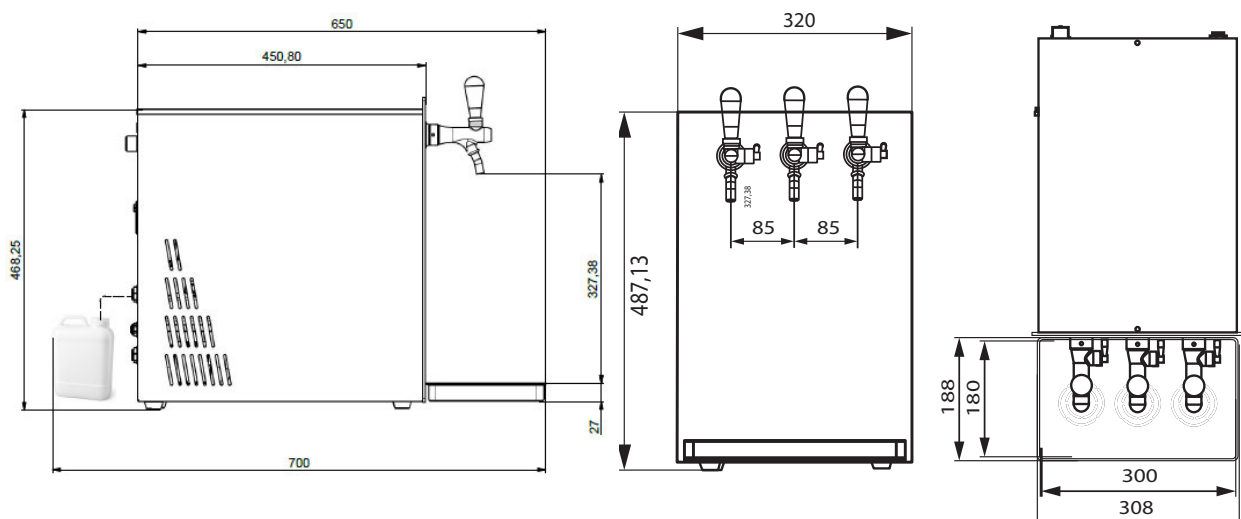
Abmessungen und Dimensionen BWT Bar 120 in Millimeter
